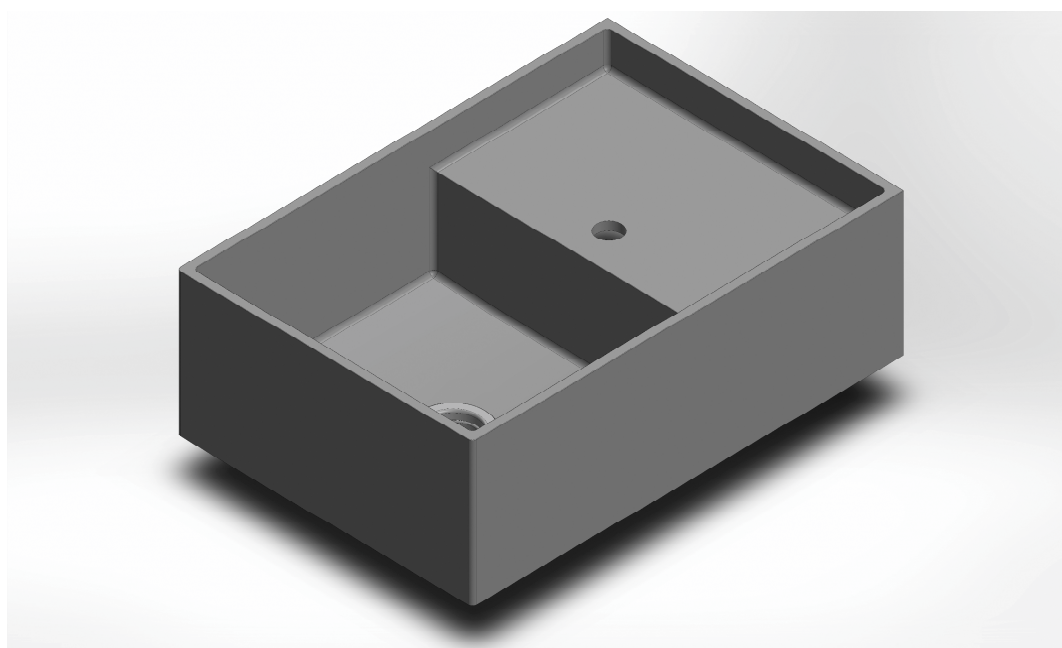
Ilustração do lava-louças proposto. Fonte da imagem: elaborada pelo autor.
